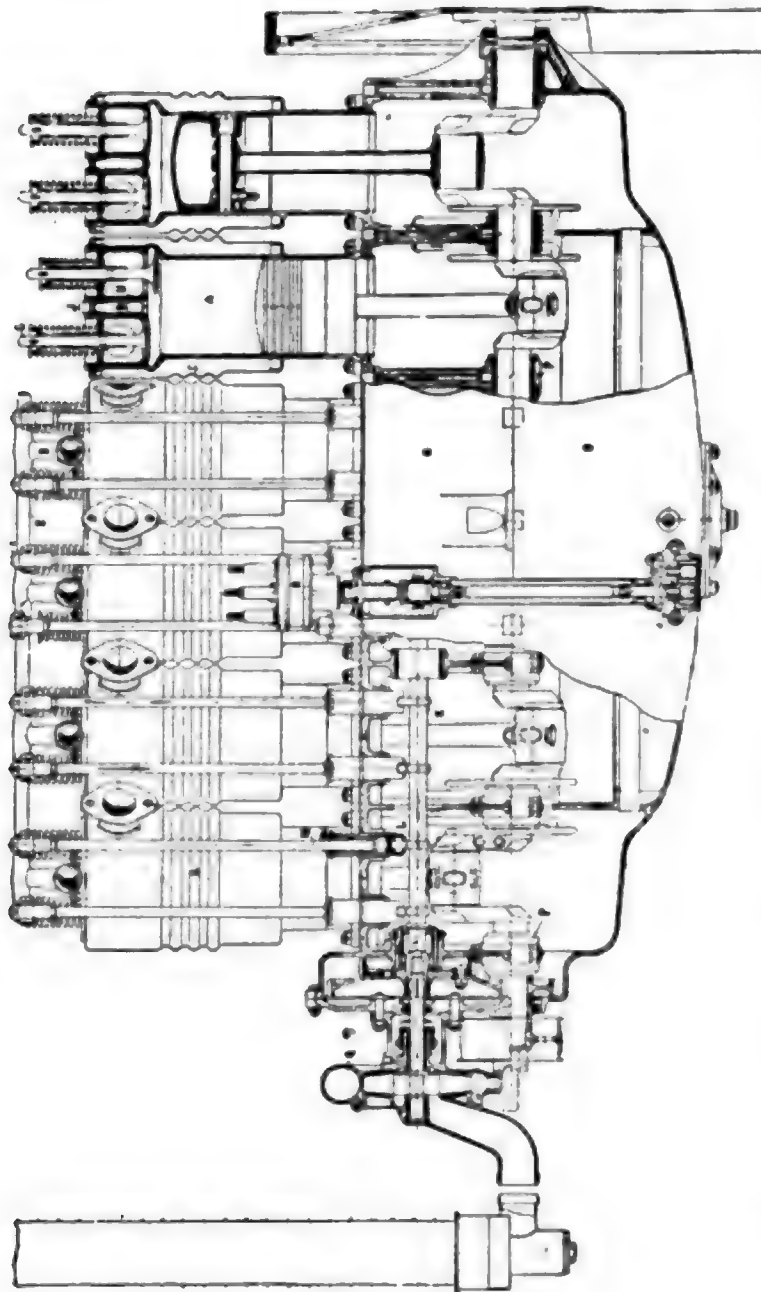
Zeichnung des „Adler“-Luftschiffmotors mit sechs Zylindern. A Zylinder, B Ventilkörbe, C Einlaßventil, H Auspuffventil, J Befestigungsmutter für die Ventilkörbe, F Ventilhebel, E Achse für Ventilhebel, D Wasserauslaß, K Steuerwelle, L Ventilstöpsel, M Stoßstangen, P Wellenlager, N Oberteil, O Unterteil des Kurbelgehäuses, S Ölpumpe, Q Wasserpumpe.
